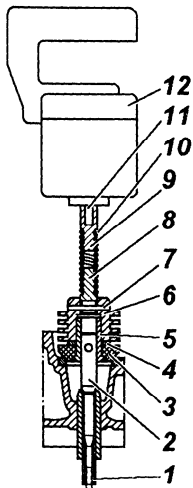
Приспособление для шлифовки седел клапанов:
